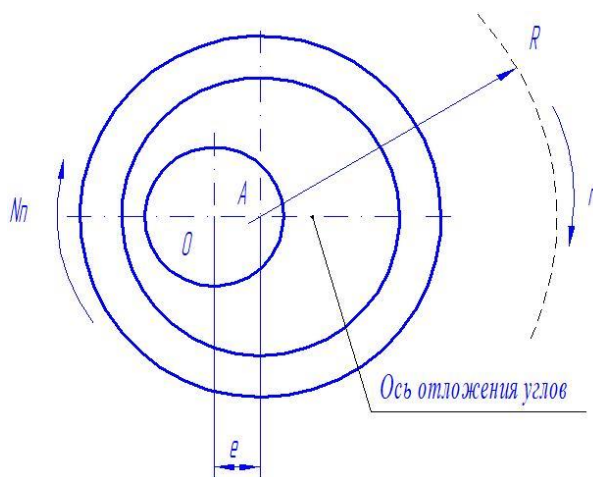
Схема инструмента для обработки изделий с зубчатым контуром
